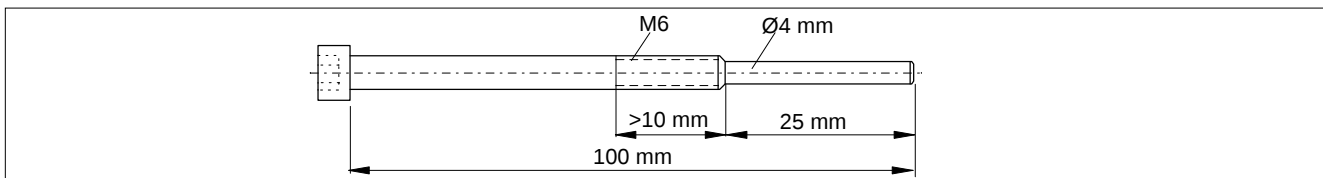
Sonderschraube für Demontage ERN 1387.001 und EQN 1325.001
